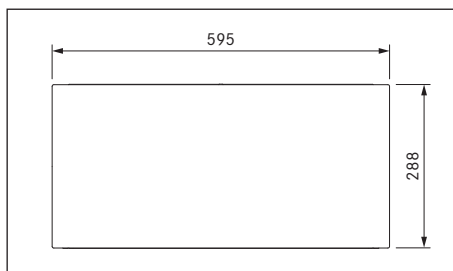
Dimensões do aparelho MSS290, vista frontal
